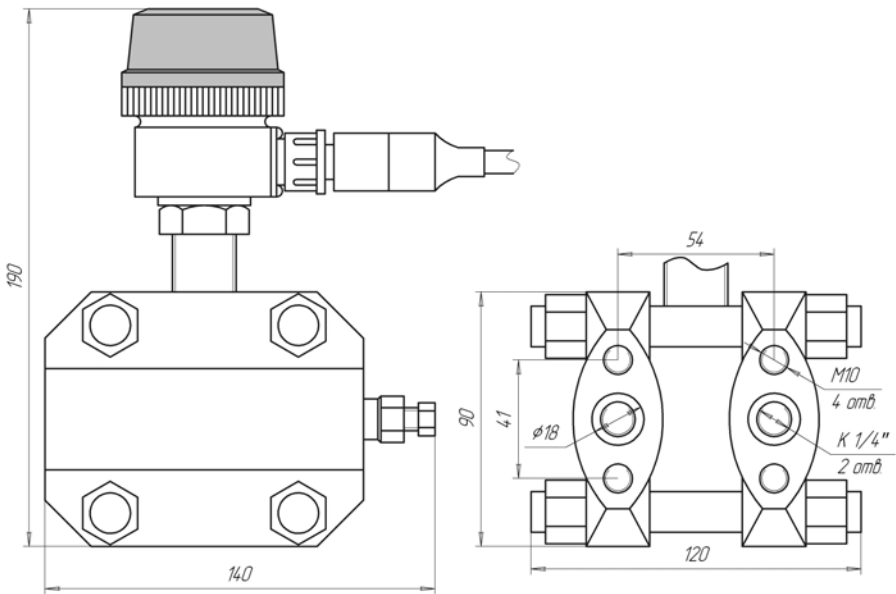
Модель 1168. Нержавеющий корпус, герморазъем.
